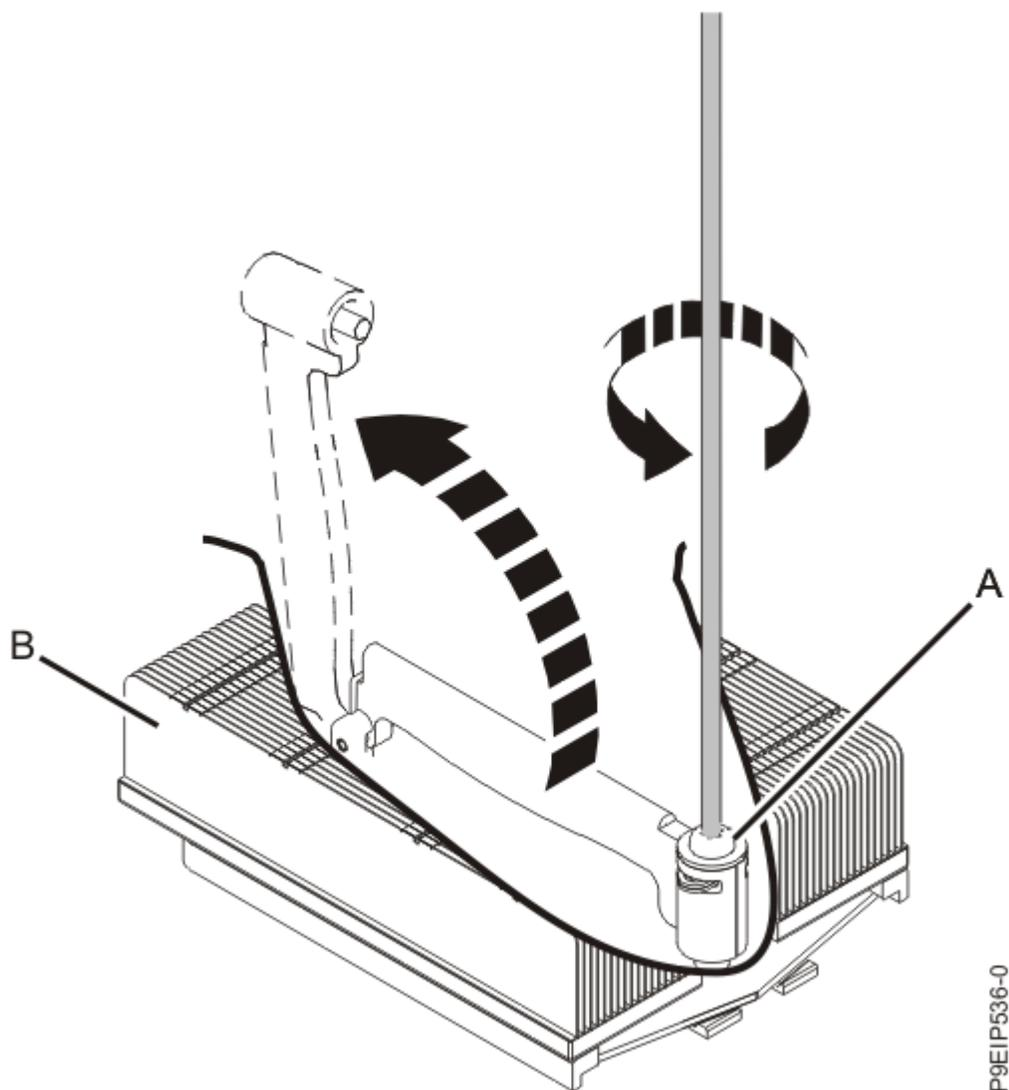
Desserrage de la vis du bras de chargement du dissipateur thermique
